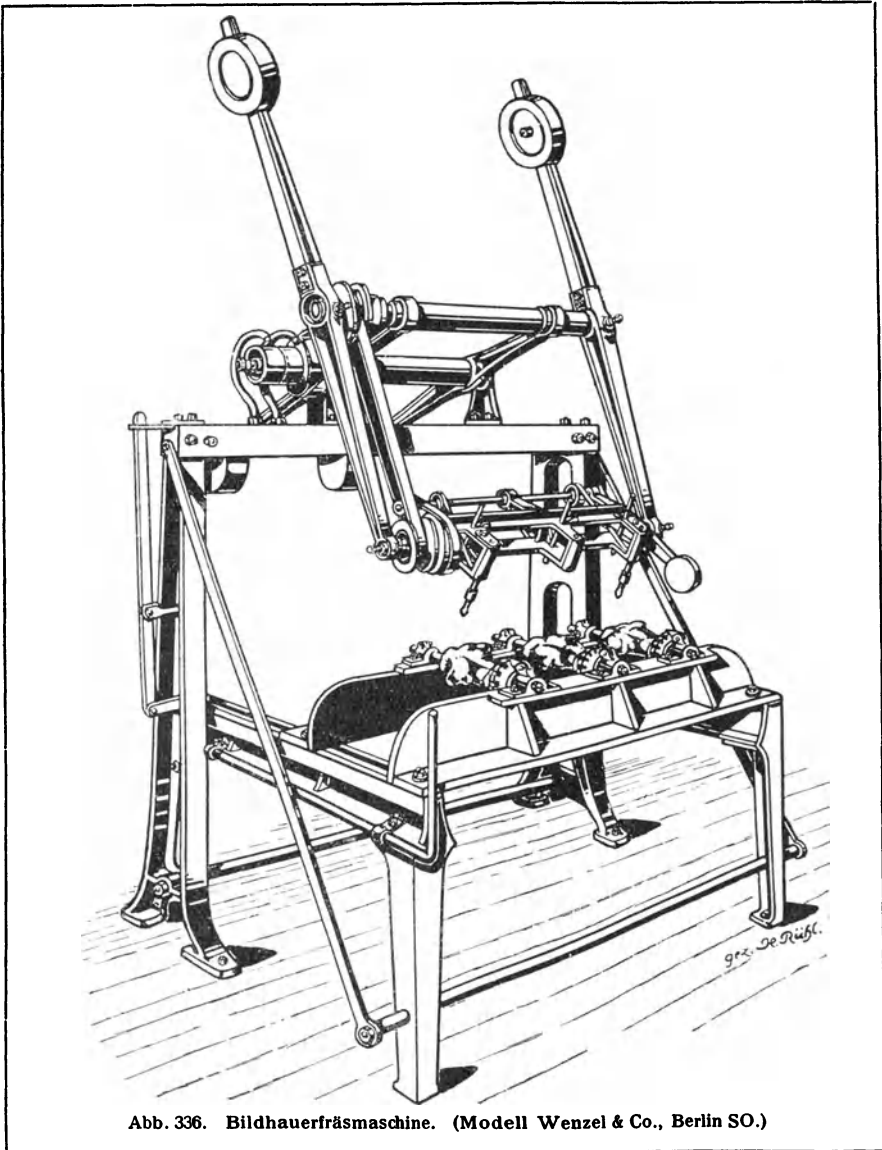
Bildhauerfräsmaschine. (Modell Wenzel & Co., Berlin SO.)
